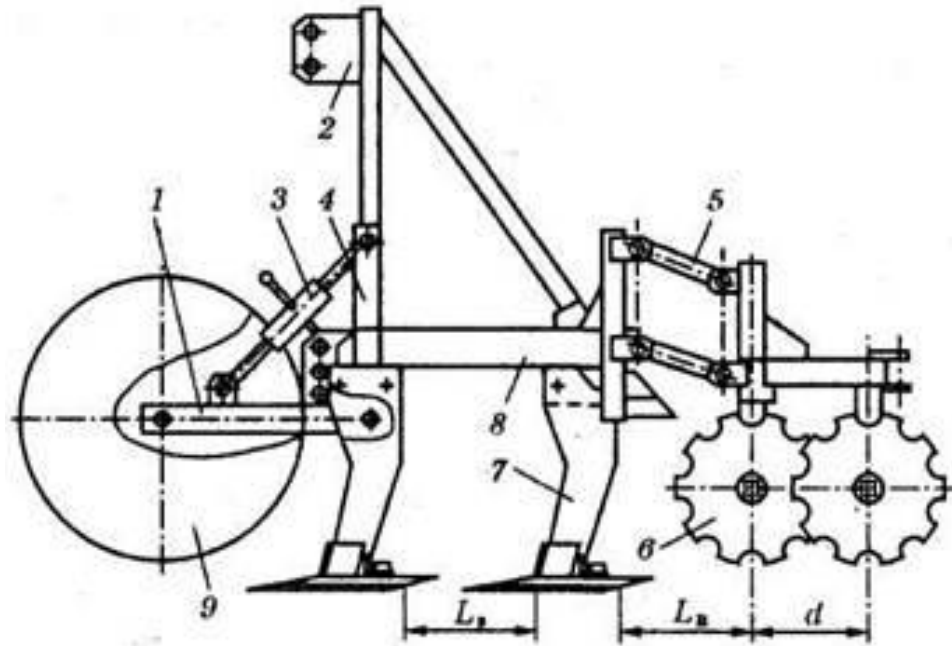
Культиватор-розпушувач КР-4,5: 1 – повінець колеса; 2 – начіпний пристрій; 3 – регулювальний механізм; 4 – стояк; 5 – повінець дискового розпушувача; 6 – батарея дисків; 7 – плоскорізна лапа; 8 – рама; 9 – опорне колесо.
